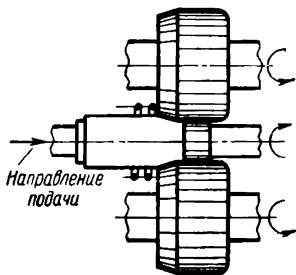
Схема накатки шестерни с осевой подачей заготовки
